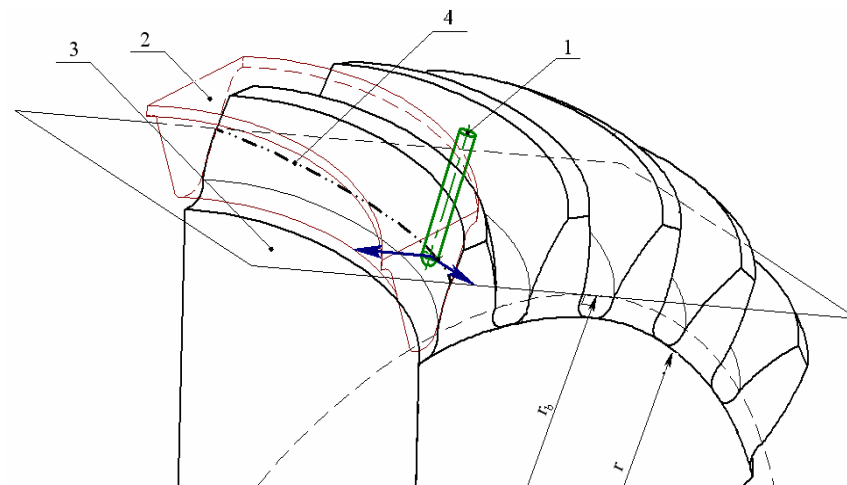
Станочное зацепление пальцевой фрезы с арочным зубом
